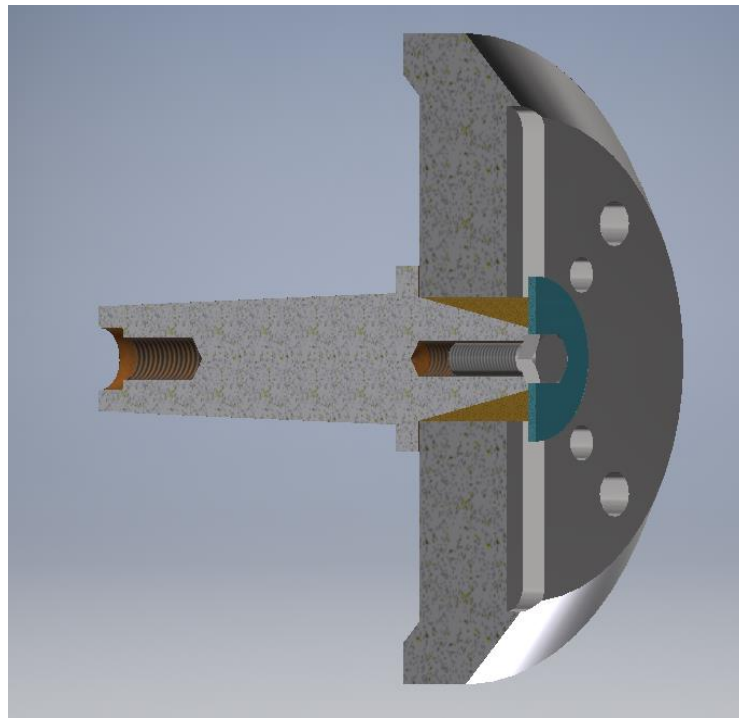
Заготовка корпусу фрези на оправці
